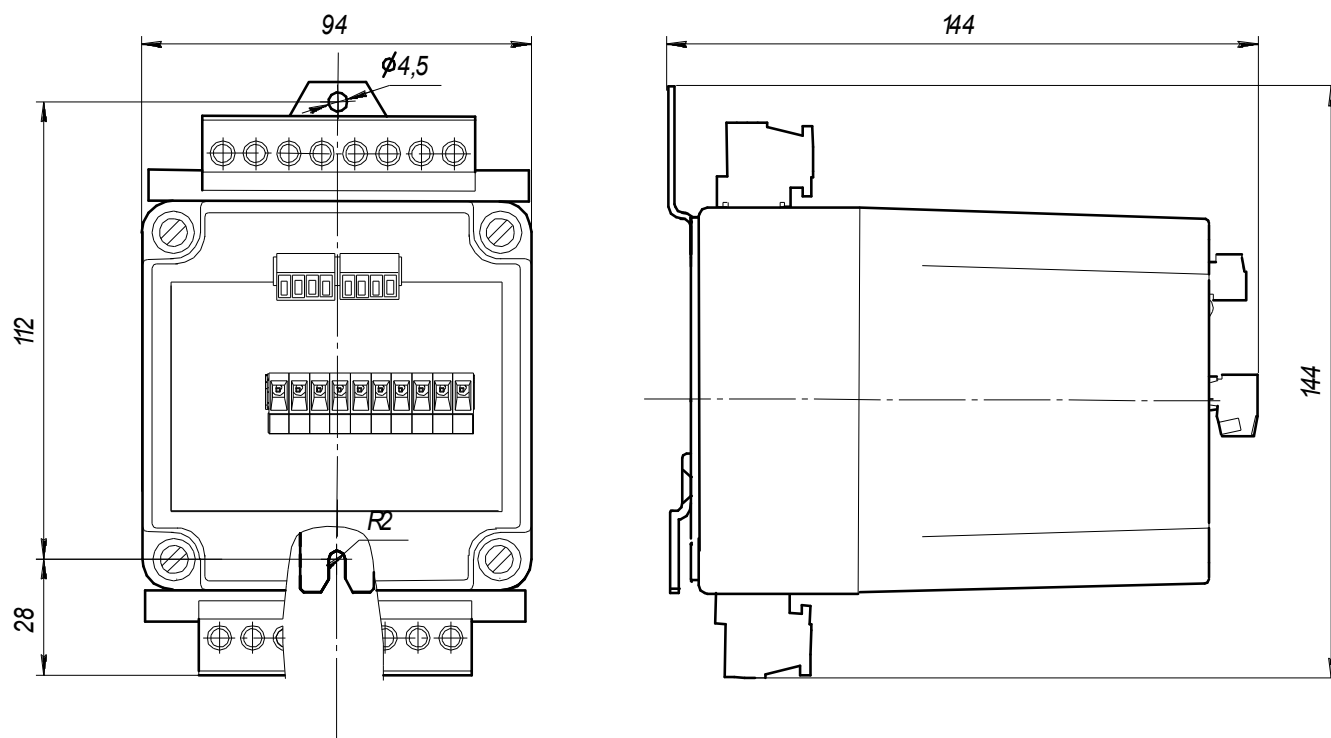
Габаритные и присоединительные размеры ПИ849Ц/XX-1 и ПИ849Ц/XX-2
